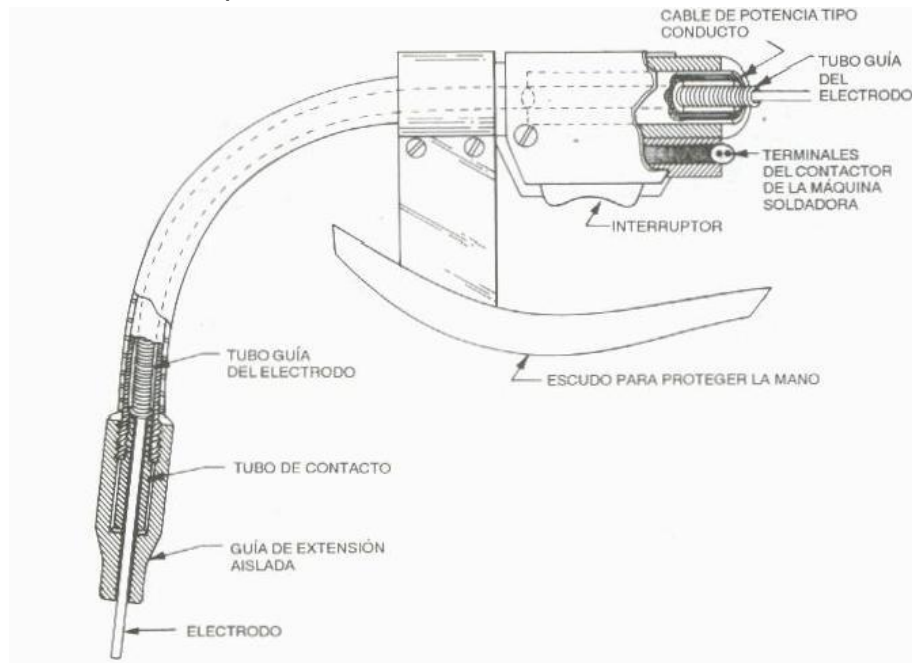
Pistolas para soldadura semiautomática
